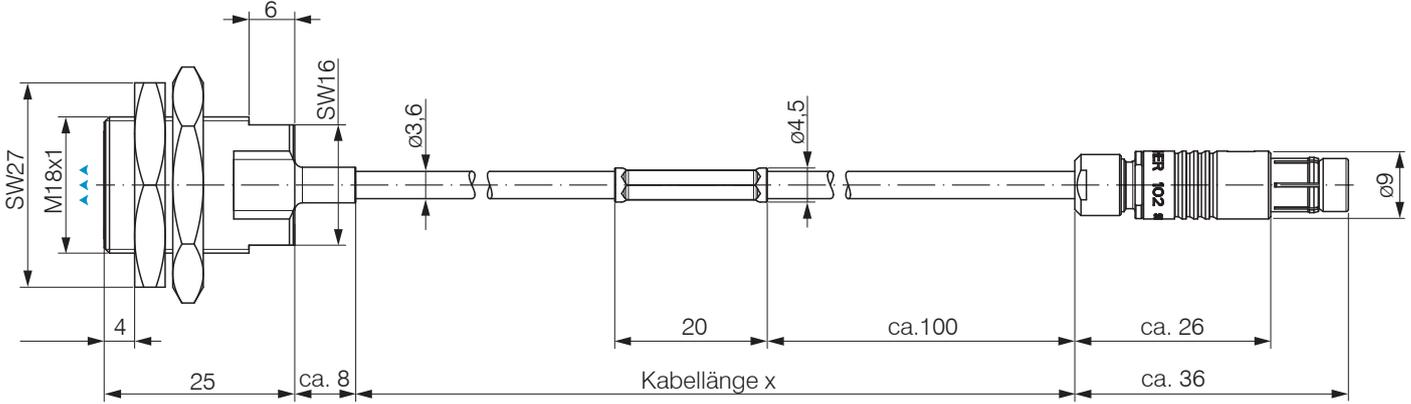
Maßzeichnung Sensoren ES-S4-C-CAx/mB0, Abmessung in mm
